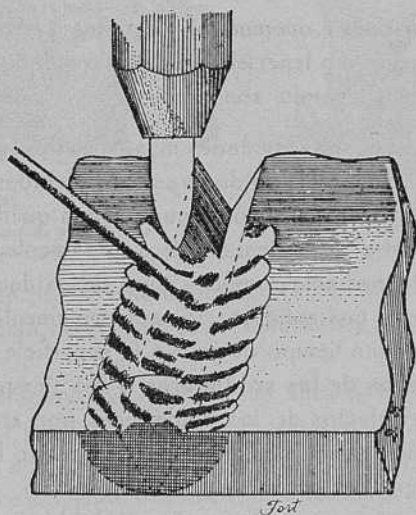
Soldadura hacia atrás en planchas gruesas.
